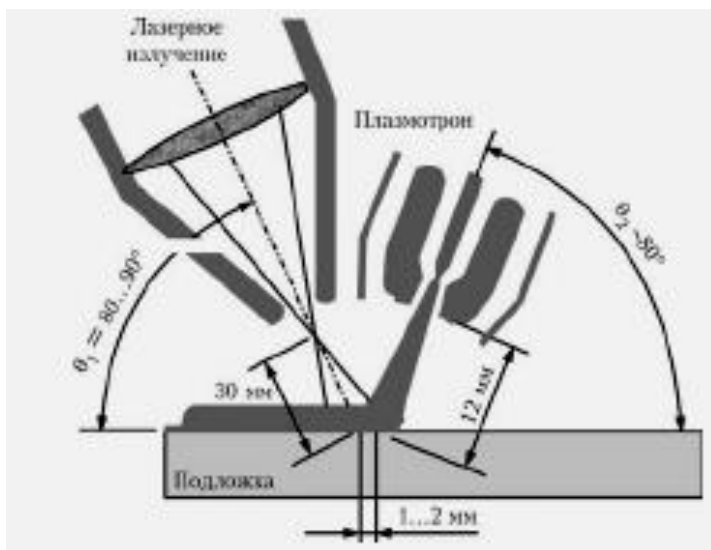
Схема гибридного лазерно-плазменного способа наплавки
